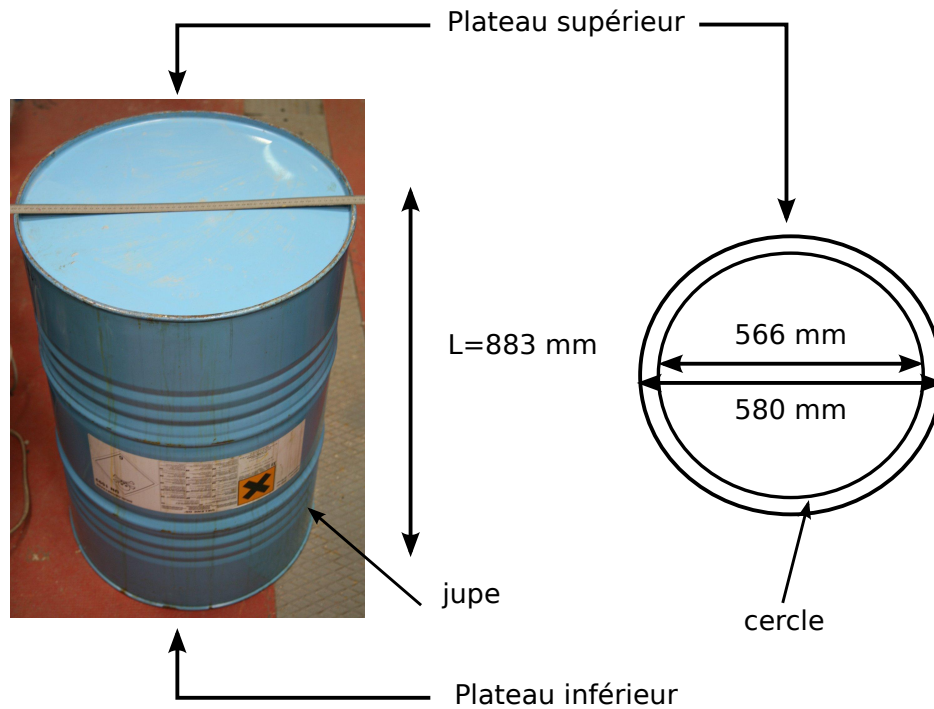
Dimensions du fût métallique destiné à la fabrication du steelpan.
